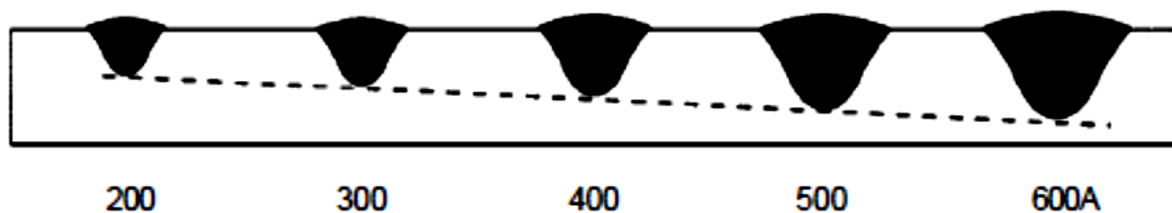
Efecto de la corriente en una soldadura [23].
